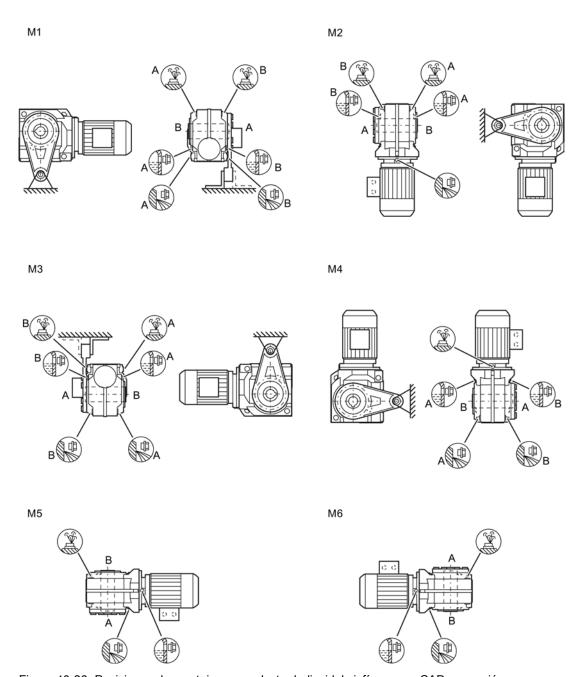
Posiciones de montaje para reductor helicoidal sinfín-corona CAD en versión enchufable, tamaños 39 - 89
